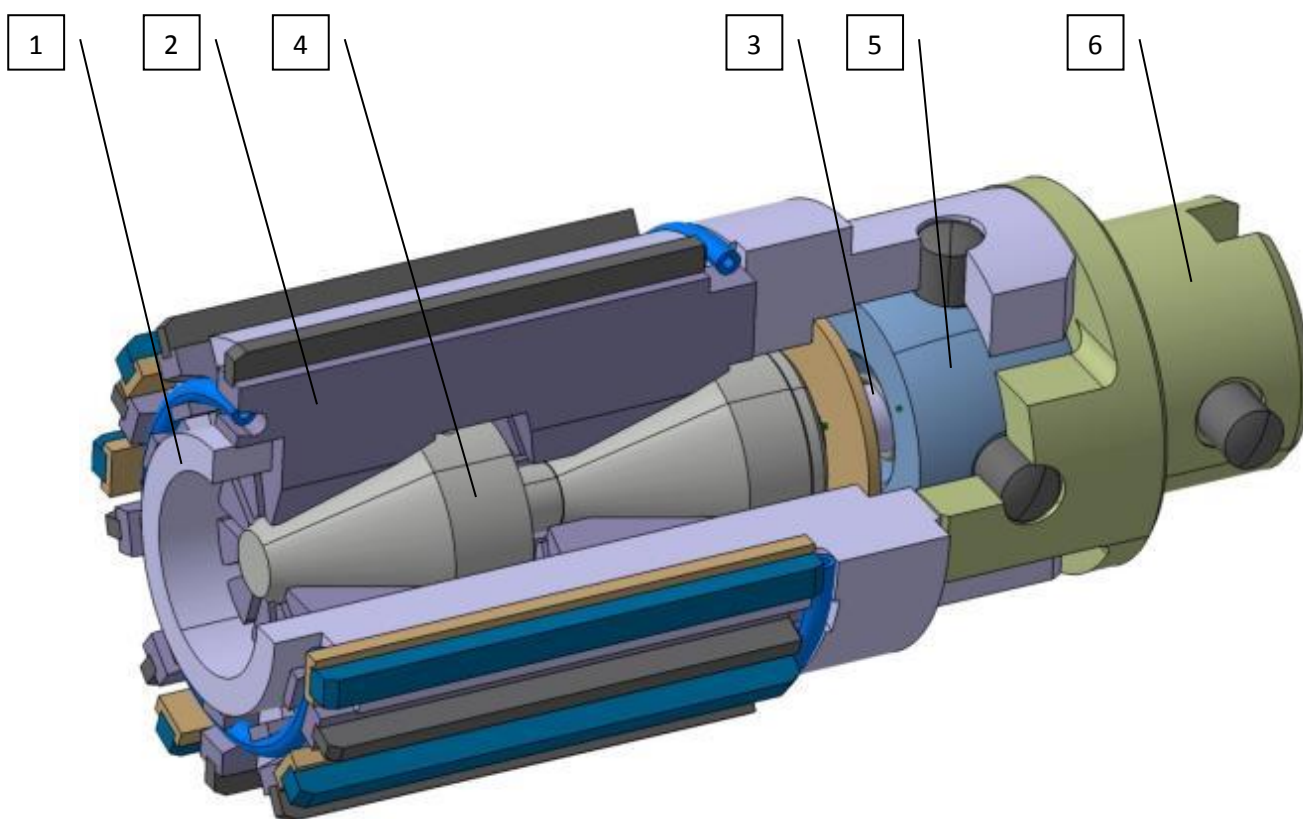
Хон для обработки блока цилиндров ДВС
